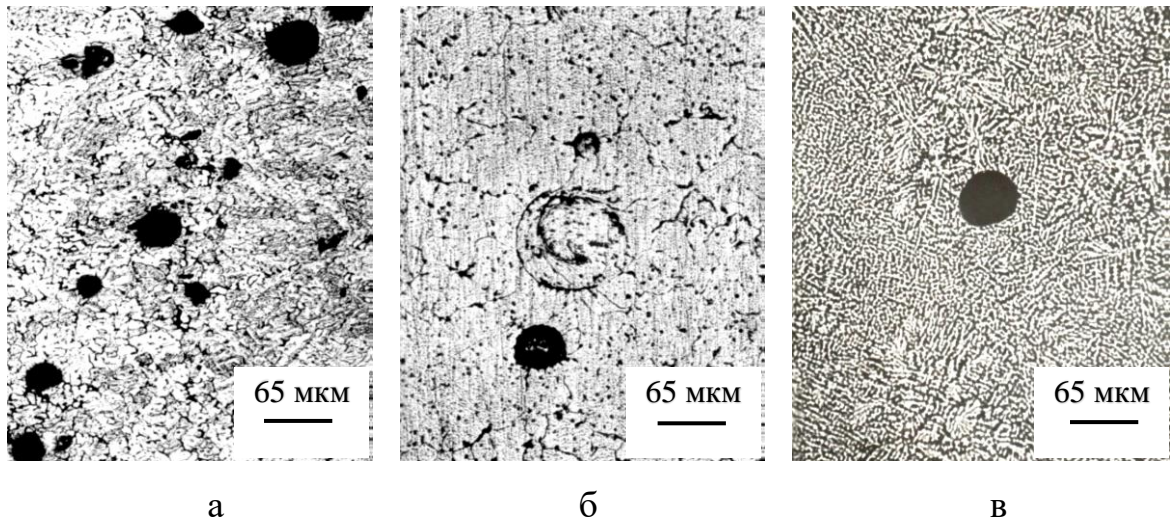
Поры в металле шва при плазменной сварке алюминиевого сплава 1565чМ ($\times 150$):
